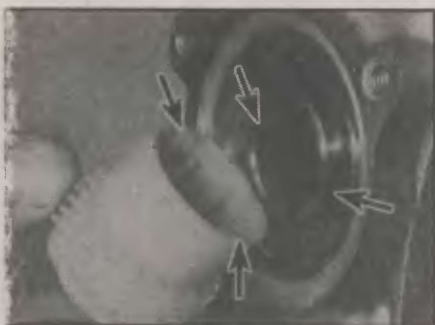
А.32. Совмещение пазов с выступами на шестерне при установке ведущей шестерни датчика скорости автомобиля
